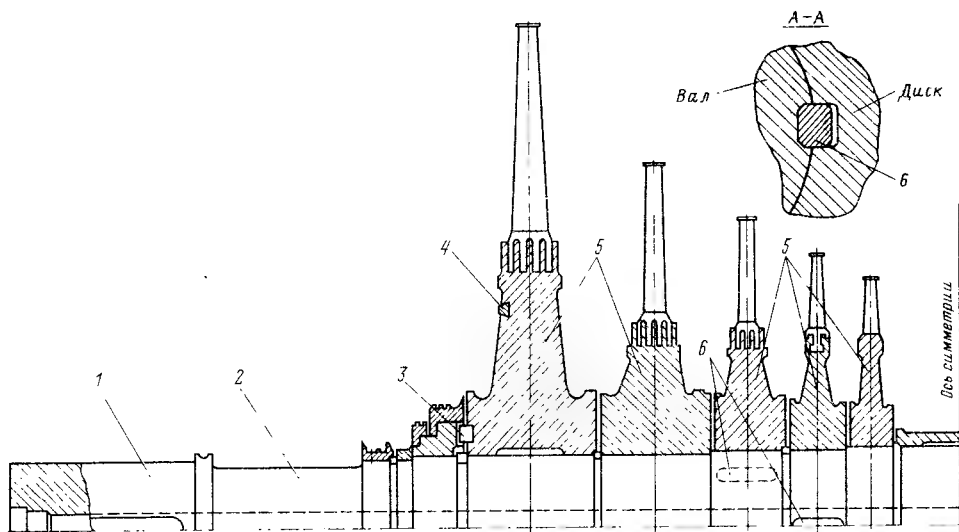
Сборный ротор двухступенчатого ЦНД.
